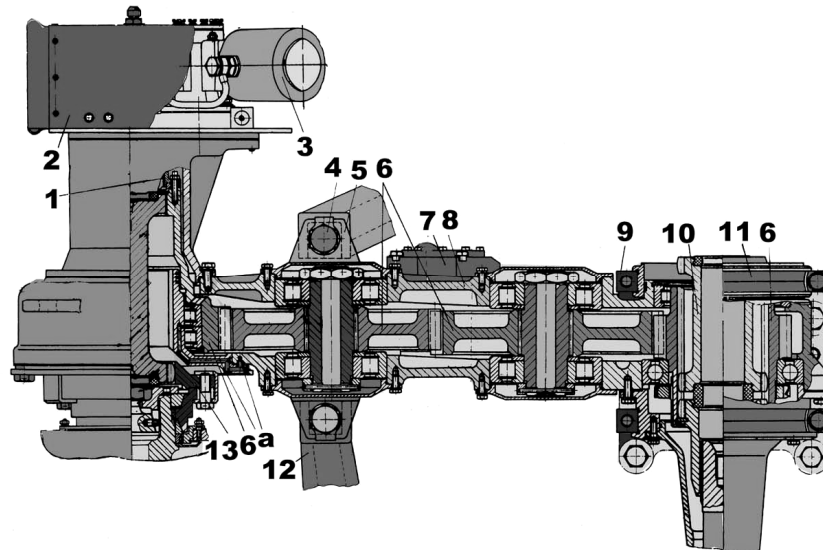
Входной редуктор: 1 – привод компрессора; 2 – кожух компрессора; 3 – компрессор; 4 – болт крепления лапы входного редуктора; 5 – лапы редуктора; 6 – шестерни; 7 – откачивающий насос; 8 – картер редуктора; 9 – бугель; 10 – детали соединения с правой КП; 11 – наметка бугеля; 12 – кронштейн; 13 – детали соединения с двигателем; а – сверление
